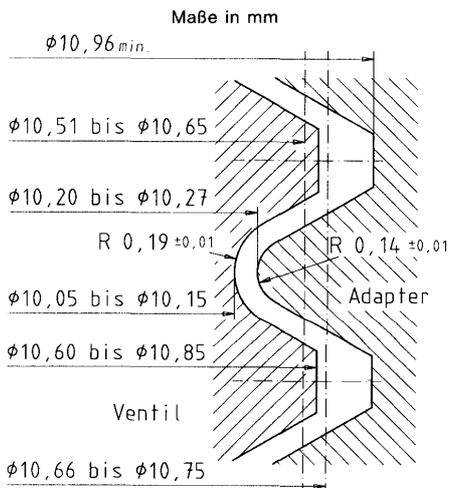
Gewindetoleranzen des Ventils und des Adapters
